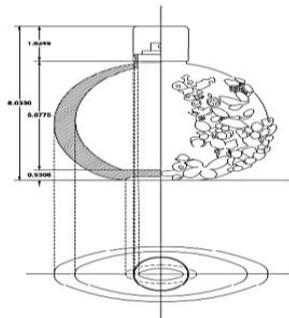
مسقط رأسي وأفقي وقطاع للفكرة التصميمية الخامسة
